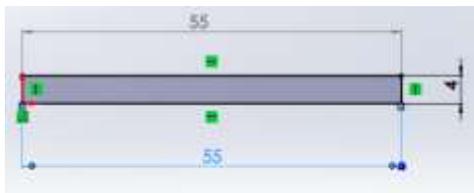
2Dimensi Hollow stainless steel 65 cm
